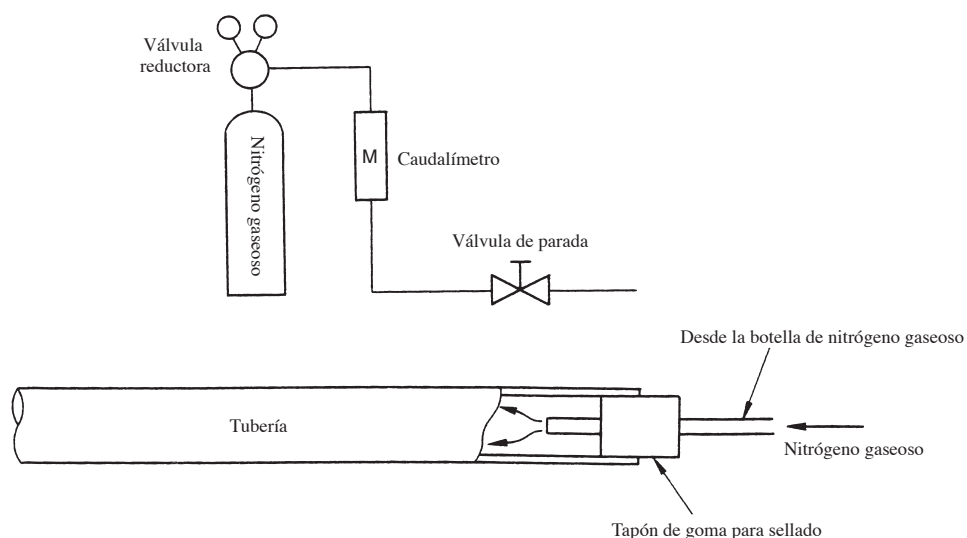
Prevención de la oxidación durante la soldadura
